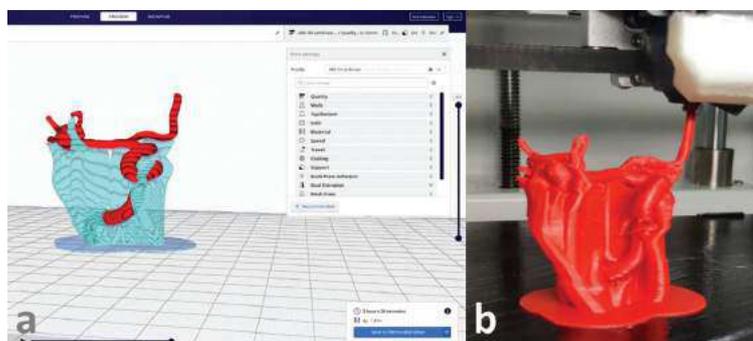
A. decomposição do arquivo .STL em finas camadas transversais; B. construção física do modelo, empilhando uma camada sobre a outra.
